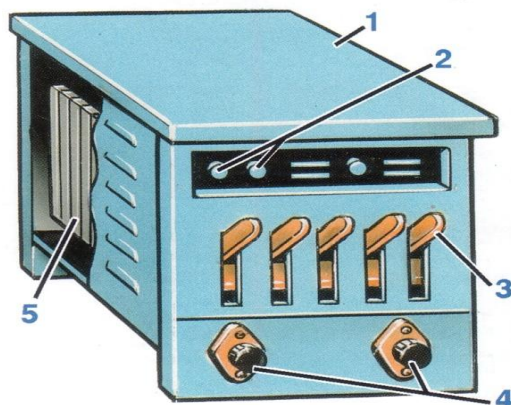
Внешний вид балластного реостата: 1 – корпус; 2 – тумблер диапазонов; 3 – рубильник секций сопротивления; 4 – клеммы сварочного кабеля; 5 – секции нихромовой проволоки или ленты
